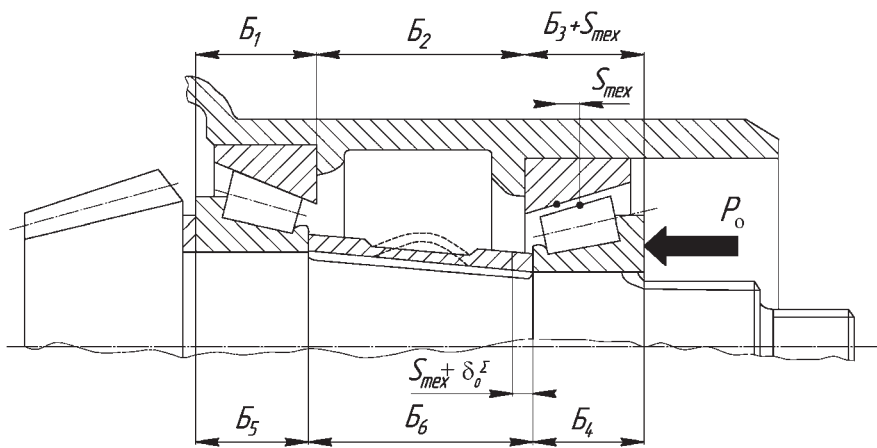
Размерная цепь подшипникового узла с деформируемой распорной втулкой
